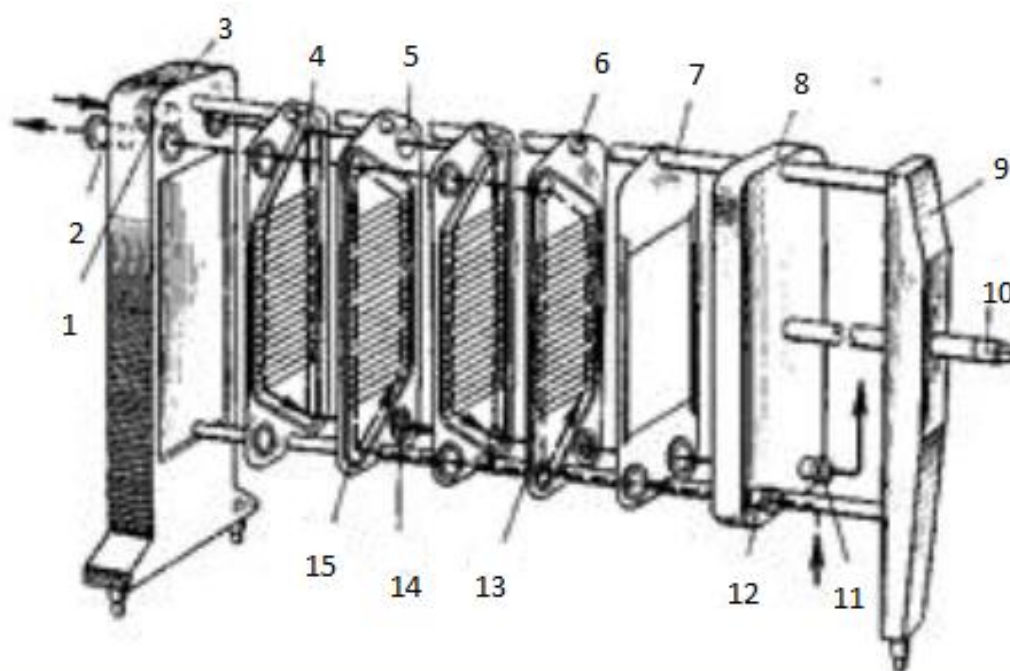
Устройство пластинчатого ТА: 1, 2, 11, 12 – штуцера; 3 – стойка передняя; 4 – угловое отверстие (верхнее); 5 – прокладка кольцевая резиновая; 6 – пластина граничная; 7 – штанга; 8 – плита нажимная; 9 – стойка задняя; 10 – крепежный винт; 13 – прокладка резиновая (большая); 14 – отверстие нижнее угловое; 15 – пластина.
